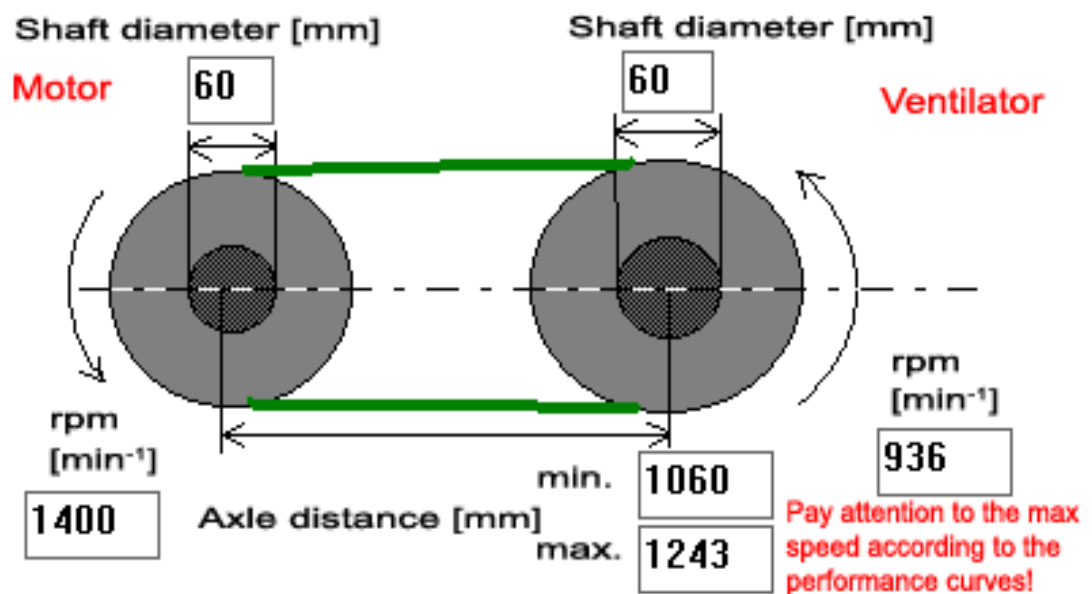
Dimensiones de la soplante del modelo CHVN 800.
